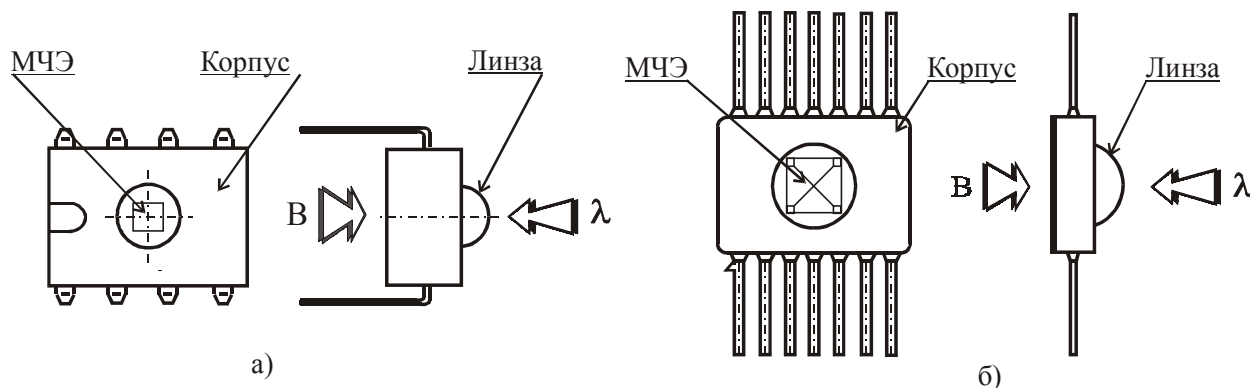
Внешний вид одноканальных магнитооптических микросхем: а – в пластмассовом корпусе; б – в металлокерамическом корпусе
